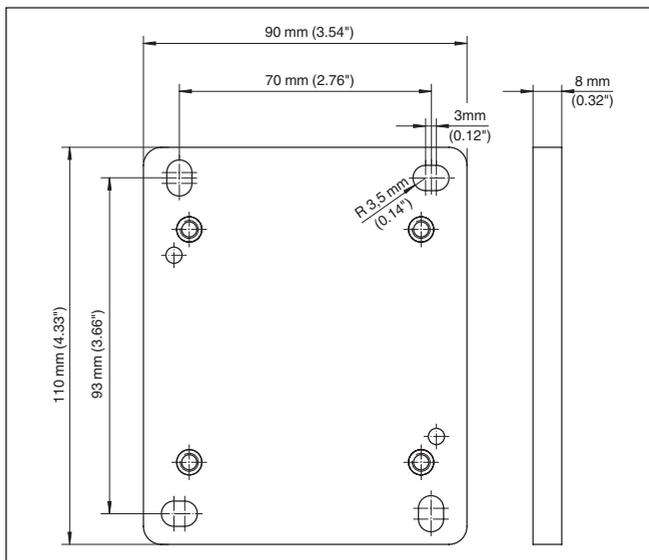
Gabarito dos orifícios - Placa de montagem na parede
